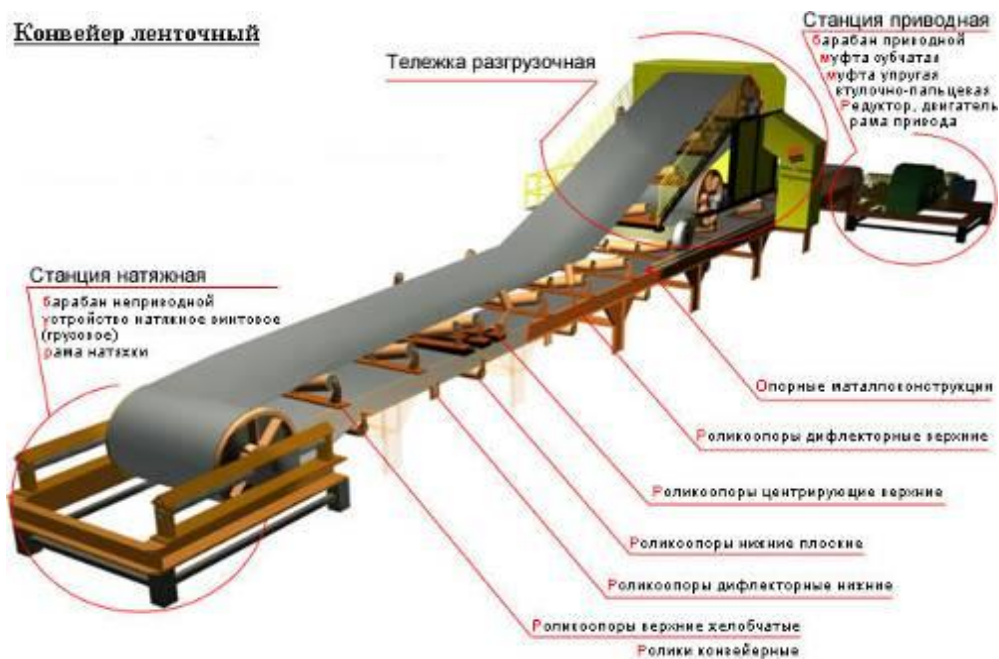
Типова конструкція стрічкового конвейера
